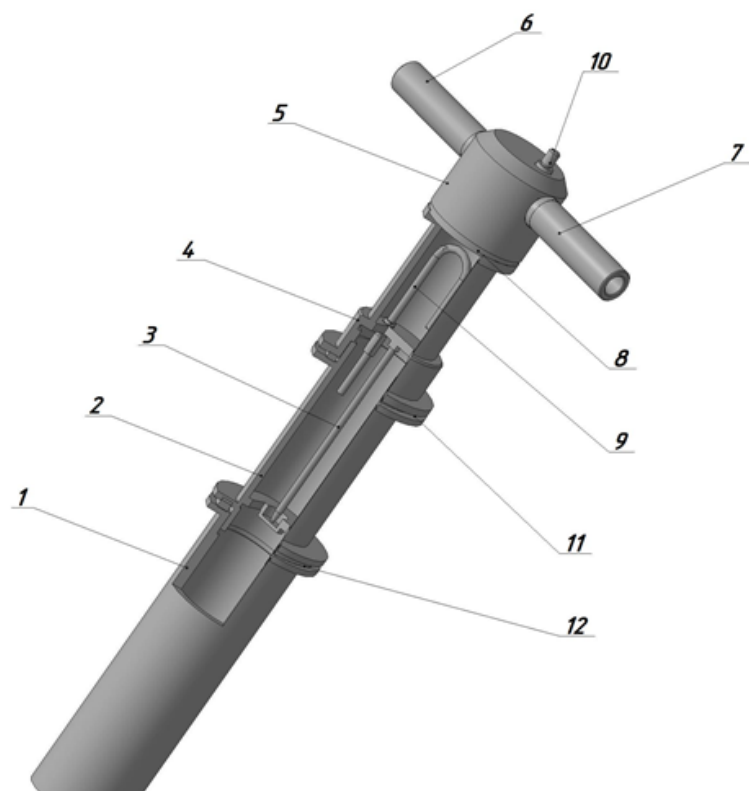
Пример выполнения газогенератора для мобильной беспрессовой газодетонационной штамповки (имитационная модель): 1 – корпус; 2 – корпус для реагента (воды); 3 – выталкиватель герметизирующего элемента; 4 – корпус активатора; 5 – газосборник; 6, 7 – трубка (подсоединительная и отводящая); 8, 11, 12 – герметизирующее кольцо; 9 – газоотводящая трубка
